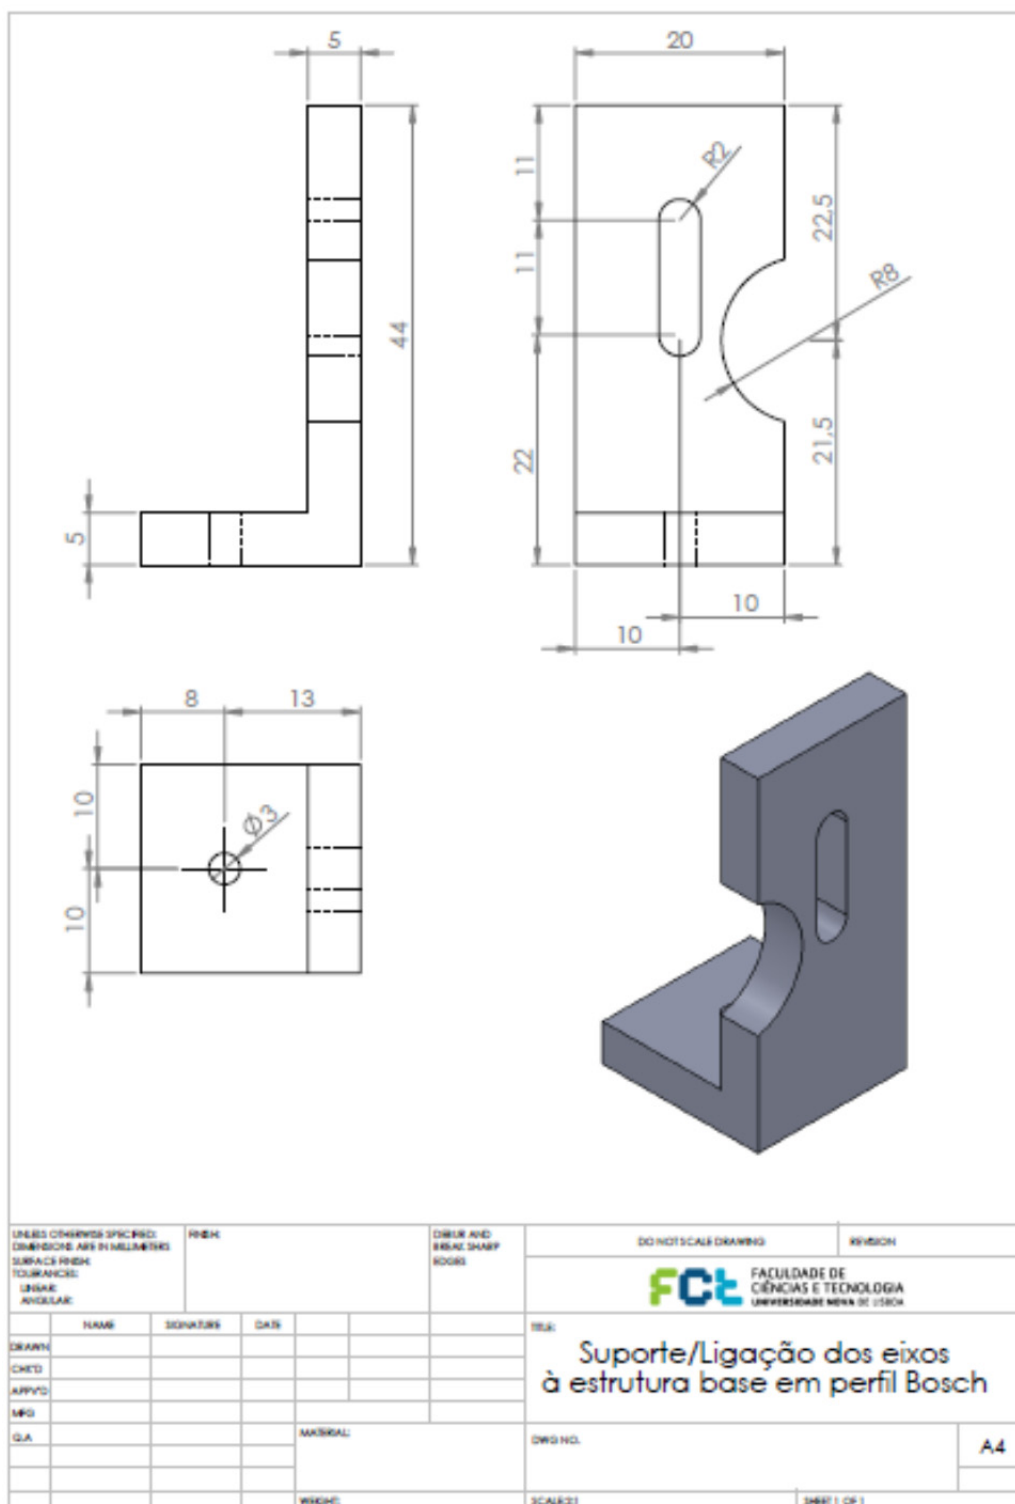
Desenho técnico do suporte que liga o barramento à estrutura base em perfil Bosch
